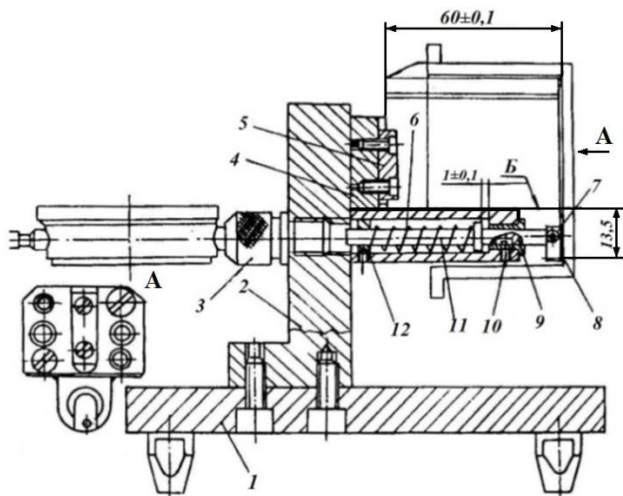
Приспособление для контроля биения внутреннего торца втулки
